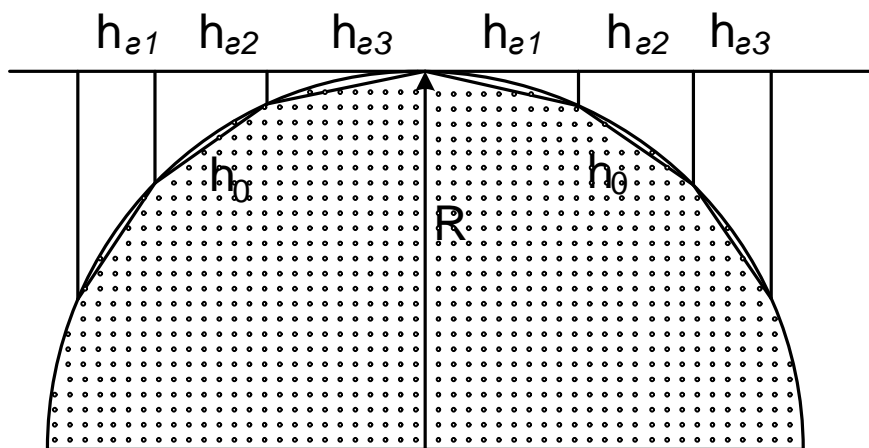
До визначення кроку виборки на поверхні зразка циліндричної форми
